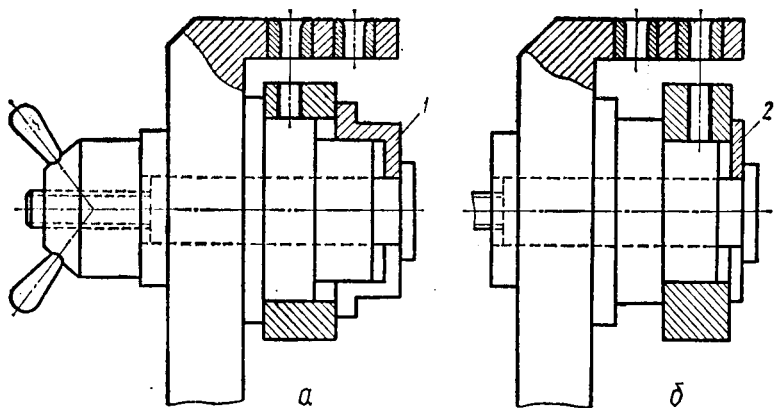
Схема кондуктора для сверления в деталях двух типоразмеров
